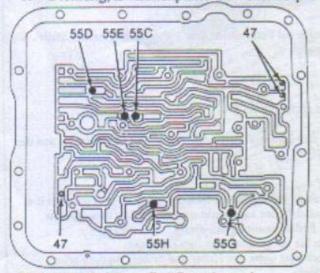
Gehäuse-Prüfkugeln und Ölschirme - Ort
